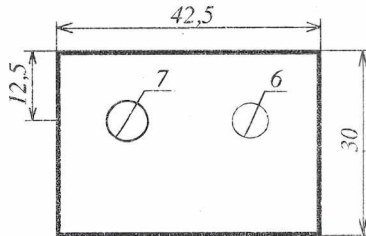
Передняя стенка корпуса (вид снаружи корпуса).
